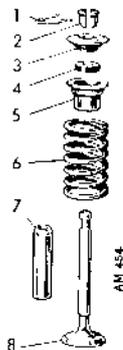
Das Bild zeigt die gesamte Ventileinheit, bestehend aus: 1 Haarnadelfeder zur Sicherung der Keile, 2 Keile, 3 Federsteller, 4 Öldichtungsring, 5 Federführung und Öldichtungsring-Halter, 6 Ventilsfeder, 7 Ventilführung, 8 Ventil
